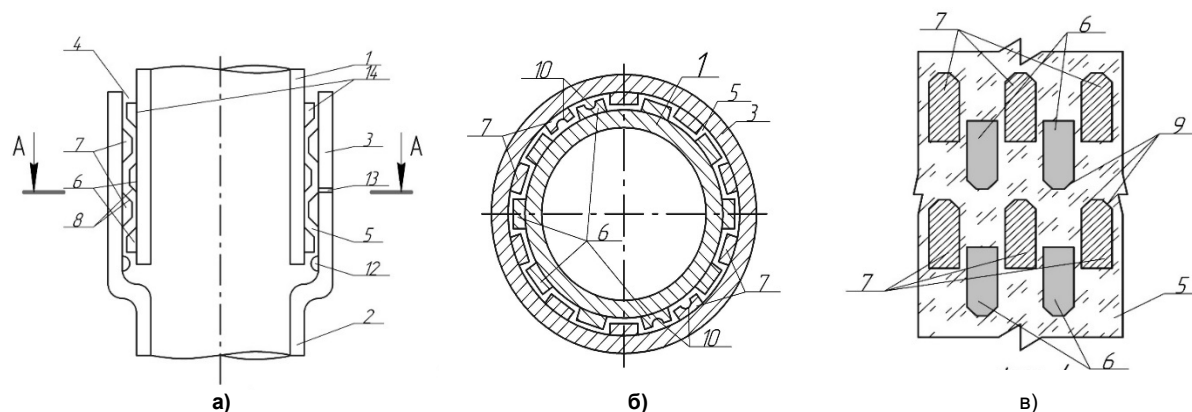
Схема стыка с внутренними раскливающе-упорными выступами: а) продольный разрез стыка; б) поперечный разрез стыка (А-А); в) развертка сопрягаемых поверхностей
